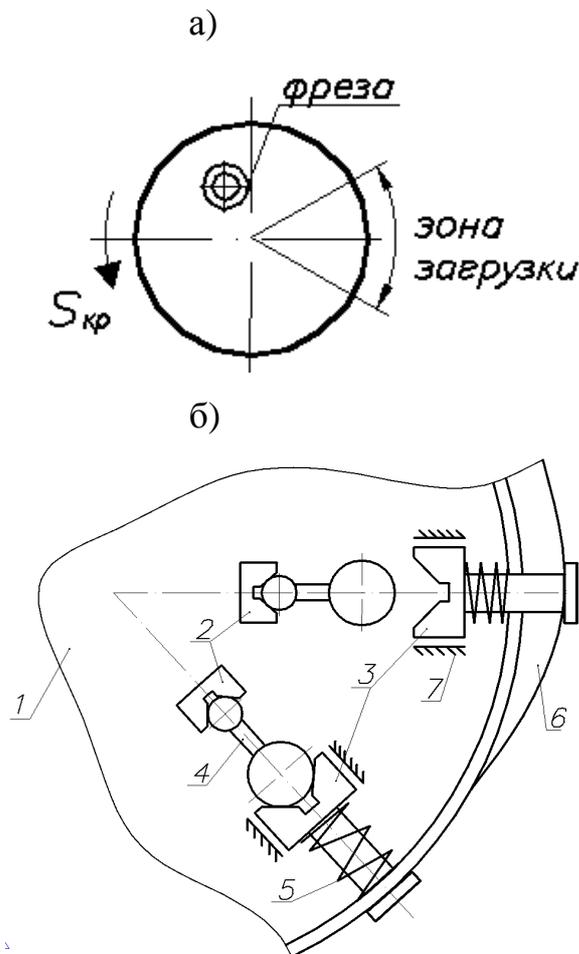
Схема приспособления для крепления заготовок на вращающемся столе 1 карусельно-фрезерного станка с автоматизированным зажимом.
